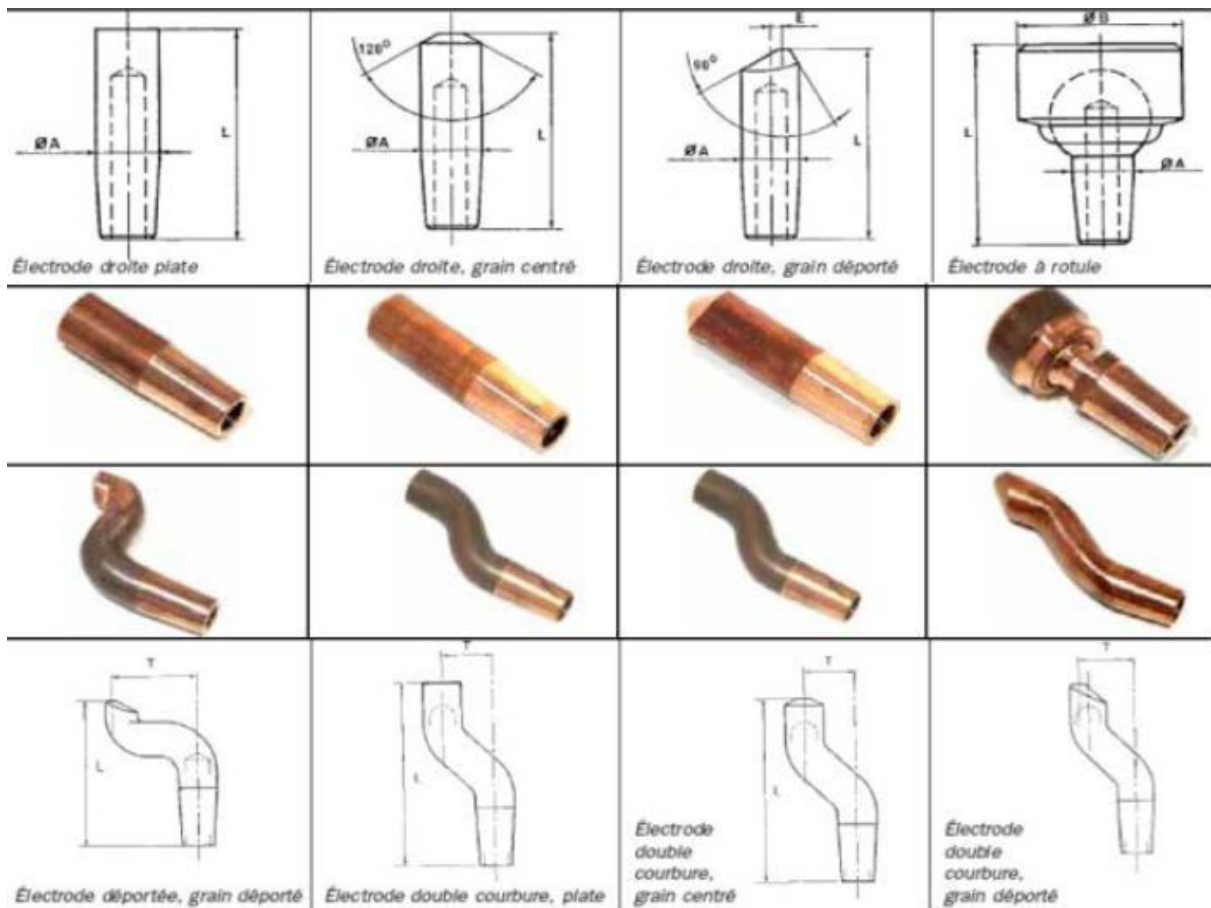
Différents formes des électrodes de la soudure par point
